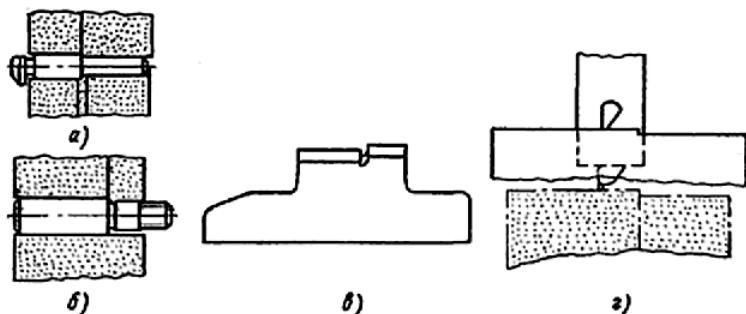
Схемы наладок для шлифования ступенчатых валков
